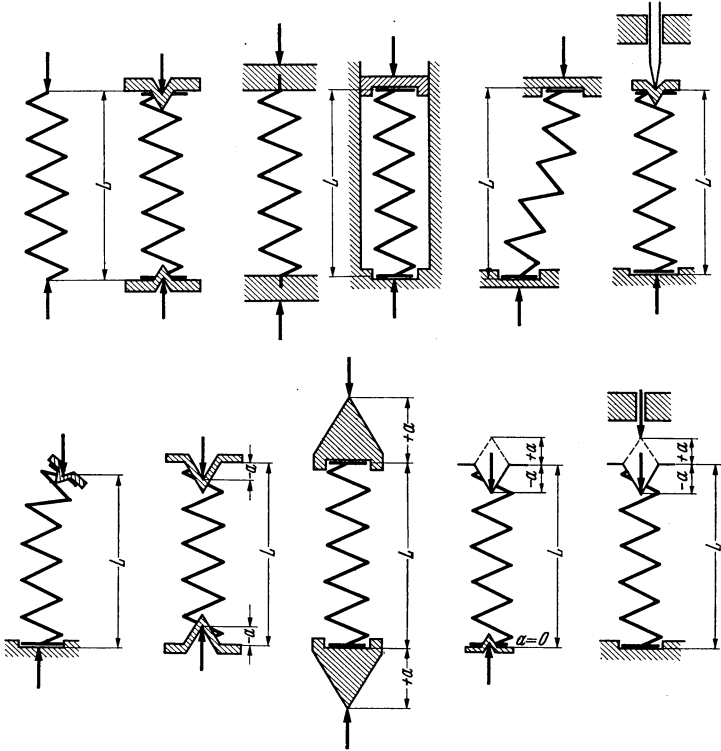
Die wichtigsten Fälle der Lagerung auf Knickung beanspruchter Schraubenfedern.
